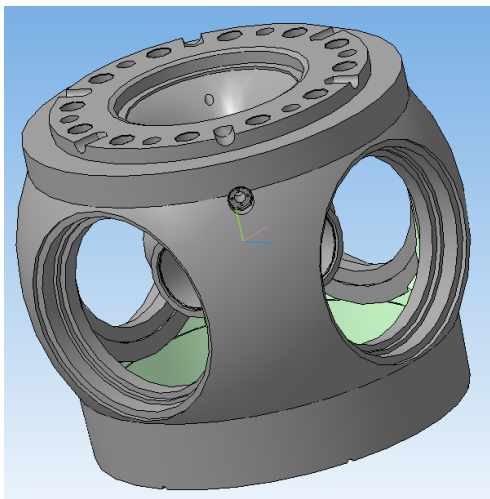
3D модель корпусу робочого колеса гідротурбіни
